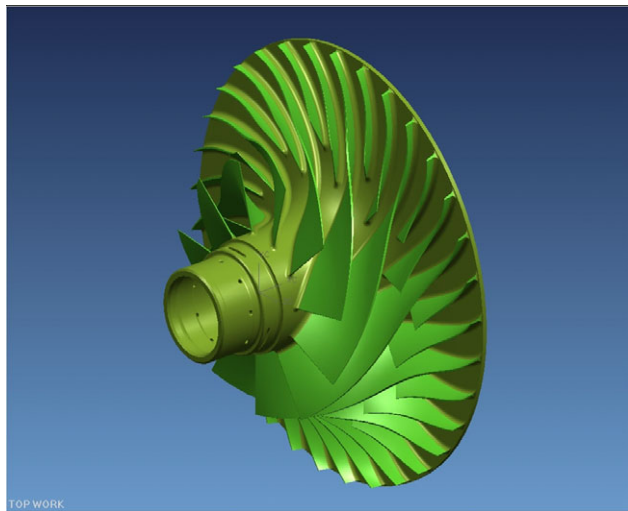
Колесо центробежного компрессора ВГТД МС-2
